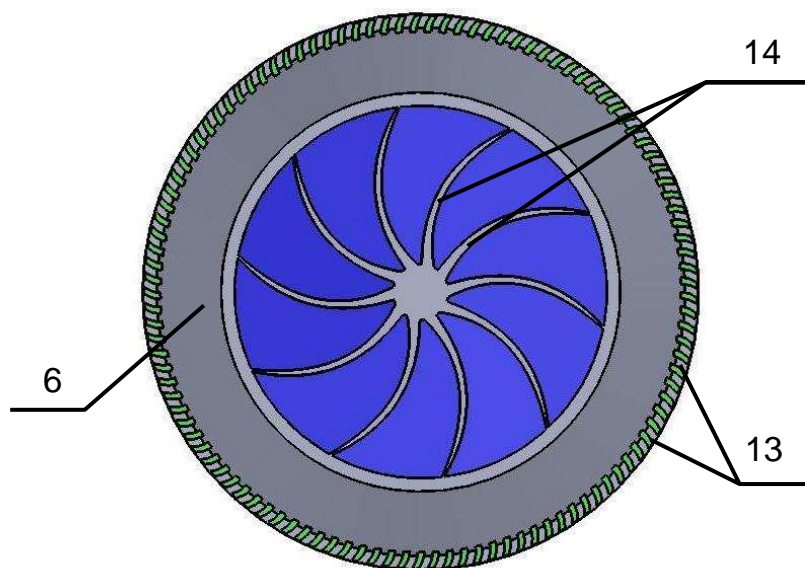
Подвижный абразивный диск с криволинейными бороздками
